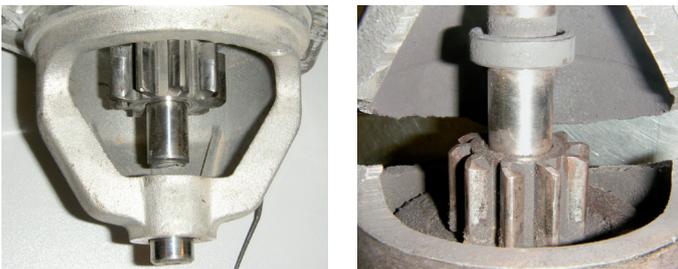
Componentes rotos de un motor de arranque: a la izquierda el árbol, a la derecha la carcasa
